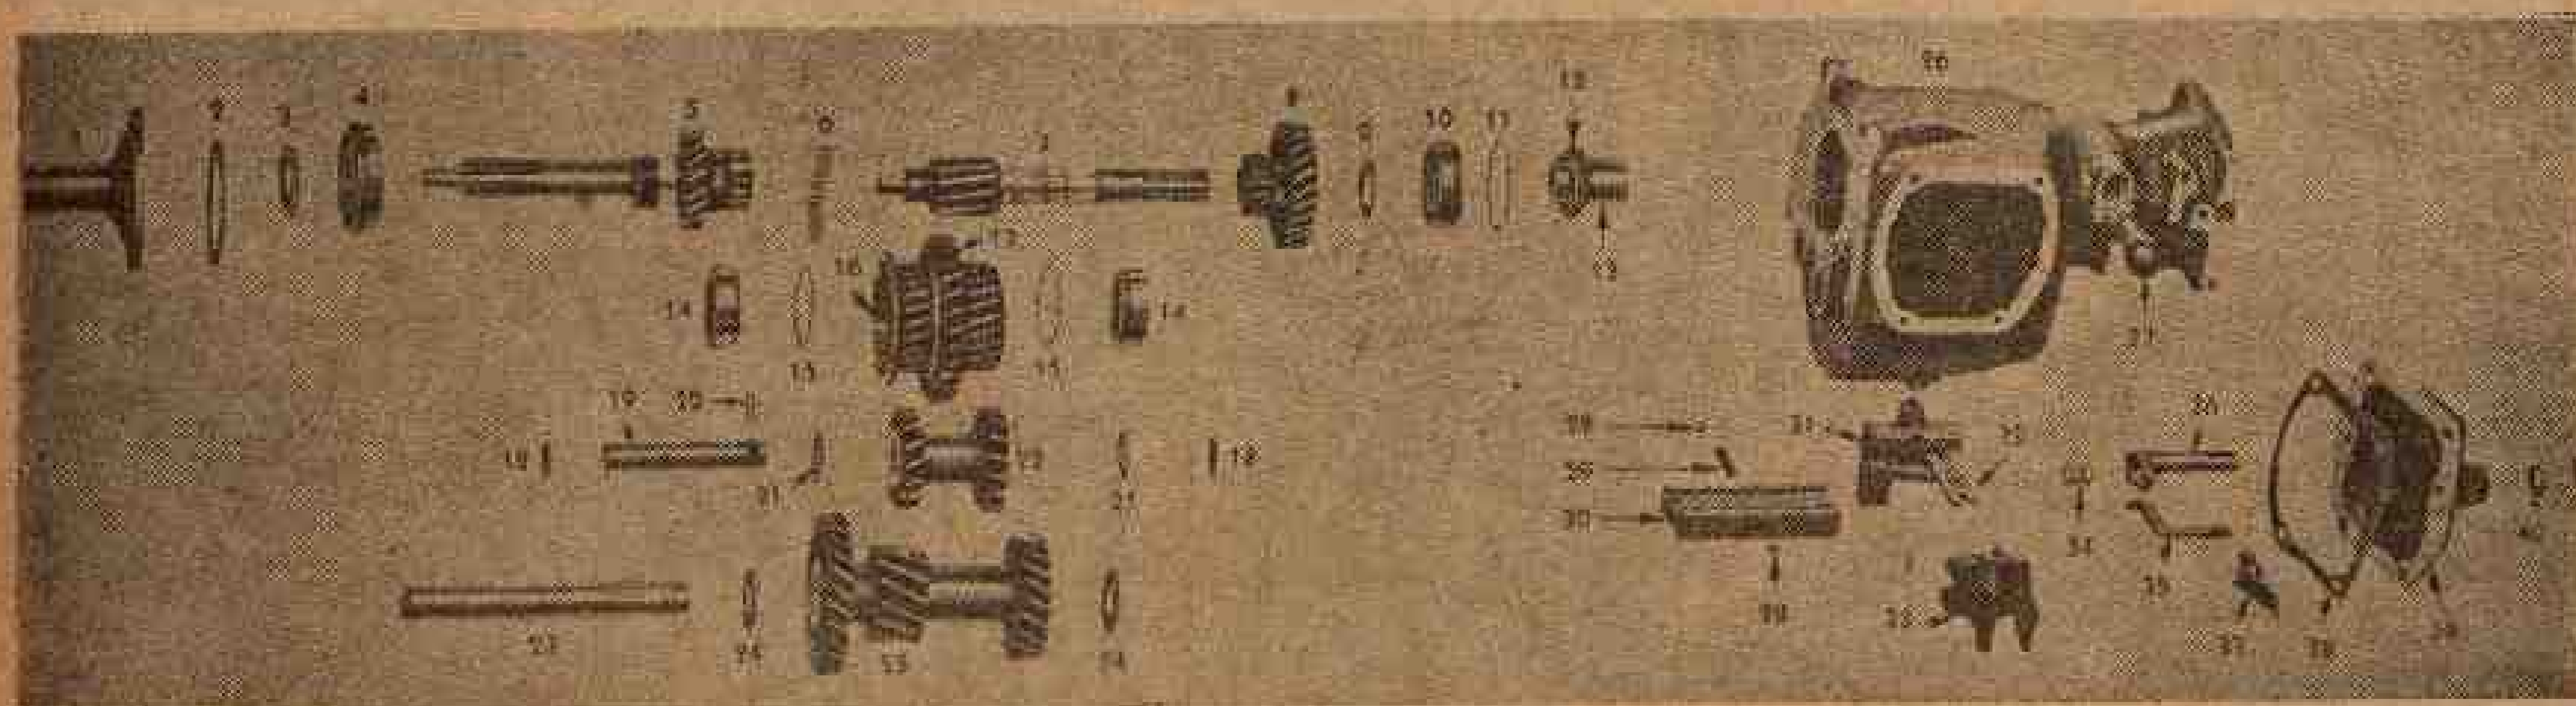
A mesma transmissão da fig. 394, desmontada, vendo-se: 1 — Retentor do mancal da embreagem, 2 — Gaxeta do retentor, 3 — Porca do mancal e barrilador de óleo, 4 — Mancal da embreagem, 5 — Engrenagem da embreagem, 6 — Mancal de agulha, 7 — Eixo principal, 8 — Engrenagem de Segunda, 9 — Arruela de encosto traseiro da engrenagem de Segunda, 10 — Mancal traseiro do eixo principal, 11 — Anel de trava do mancal traseiro, 12 — Engrenagem acionadora do velocímetro, 13 — Espaçador da junta universal, 14 — Anel de sincronização, 15 — Retentor do anel de sincronização, 16 — Tambor de sincronização, 17 — Engrenagem de Primeira e Marcha-ré, 18 — Bujão de expansão, 19 — Eixo da engrenagem intermediária de marcha-ré, 20 — Pino de trava, 21 — Arruela de encosto, 22 — Engrenagem intermediária de marcha-ré, 23 — Contra-eixo, 24 — Arruela de encosto, 25 — Conjunto do contra-eixo, 26 — Caixa, 27 — Engrenagem secundária do velocímetro, 28 — Estora de detenção da culatra deslocadora, 29 — Mola de detenção, 30 — Barra de guia, 31 — Culatra deslocadora de Segunda e Terceira, 32 — Alavanca do deslocador, 33 — Culatra deslocadora de Primeira e Marcha-ré, 34 — Mola do eixo operador, 35 — Manivela do seletor, 36 — Eixo operador, 37 — Alavanca seletora, 38 — Gaxeta da coberta da transmissão, 39 — Coberta da transmissão, 40 — Vedação do eixo operador, 41 — Retentor da vedação.
